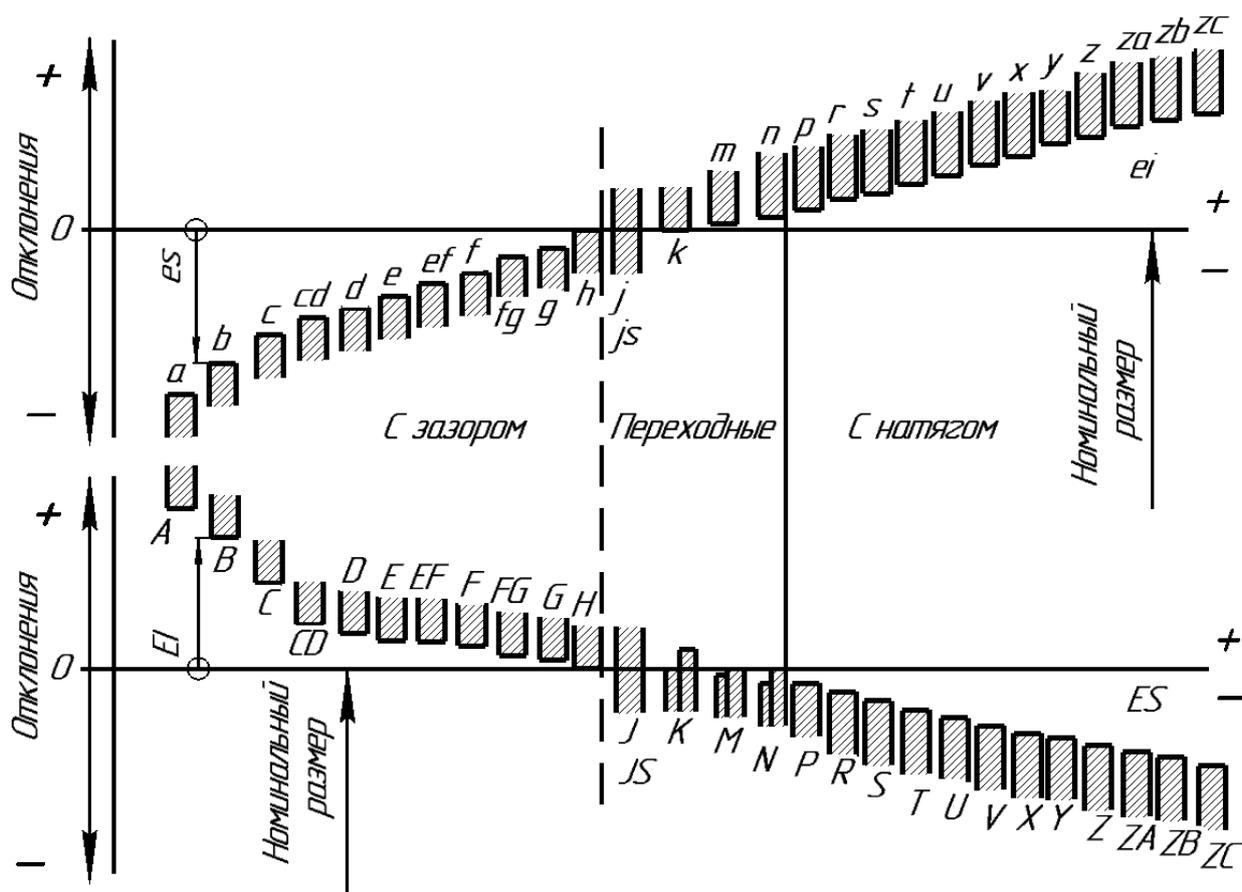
Положения интервала допуска относительно номинального размера для валов и отверстий
